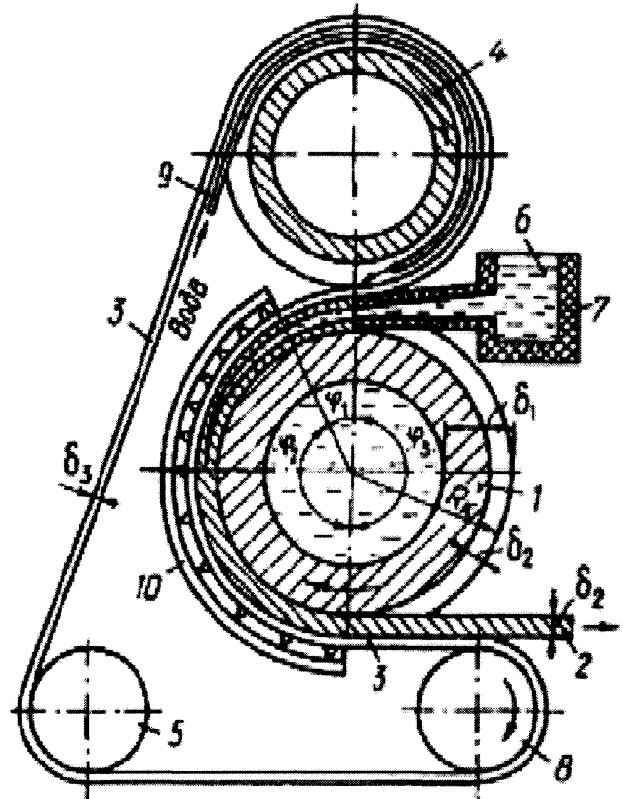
Схема непрерывного литья полосы в кристаллизатор “колесо–лента”: 1 – формообразующее колесо; 2 – отливка; 3 – рабочая лента; 4 – прижимной ролик; 5 – натяжной ролик; 6 – расплав; 7 – питатель; 8 – приводной ролик; 9 – охладитель ленты верхний; 10 – охладитель ленты боковой; R_k – внешний радиус колеса; δ_1 – толщина колеса, δ_2 – глубина ручья колеса и толщина отливки; φ_1 , φ_2 и φ_3 – расчетные зоны
